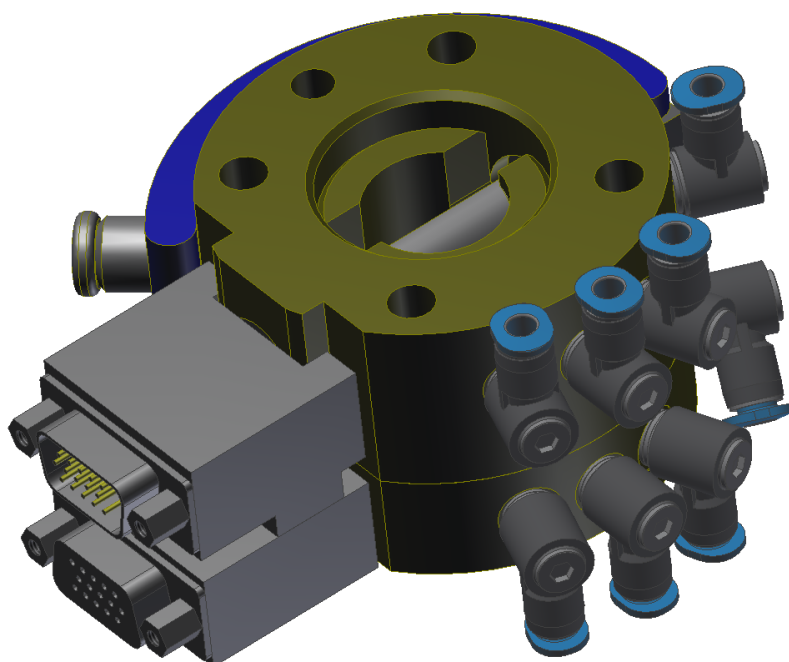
Chapadlo s mechanismem umožňujícím kompenzovat pohyb obrobku [8]
